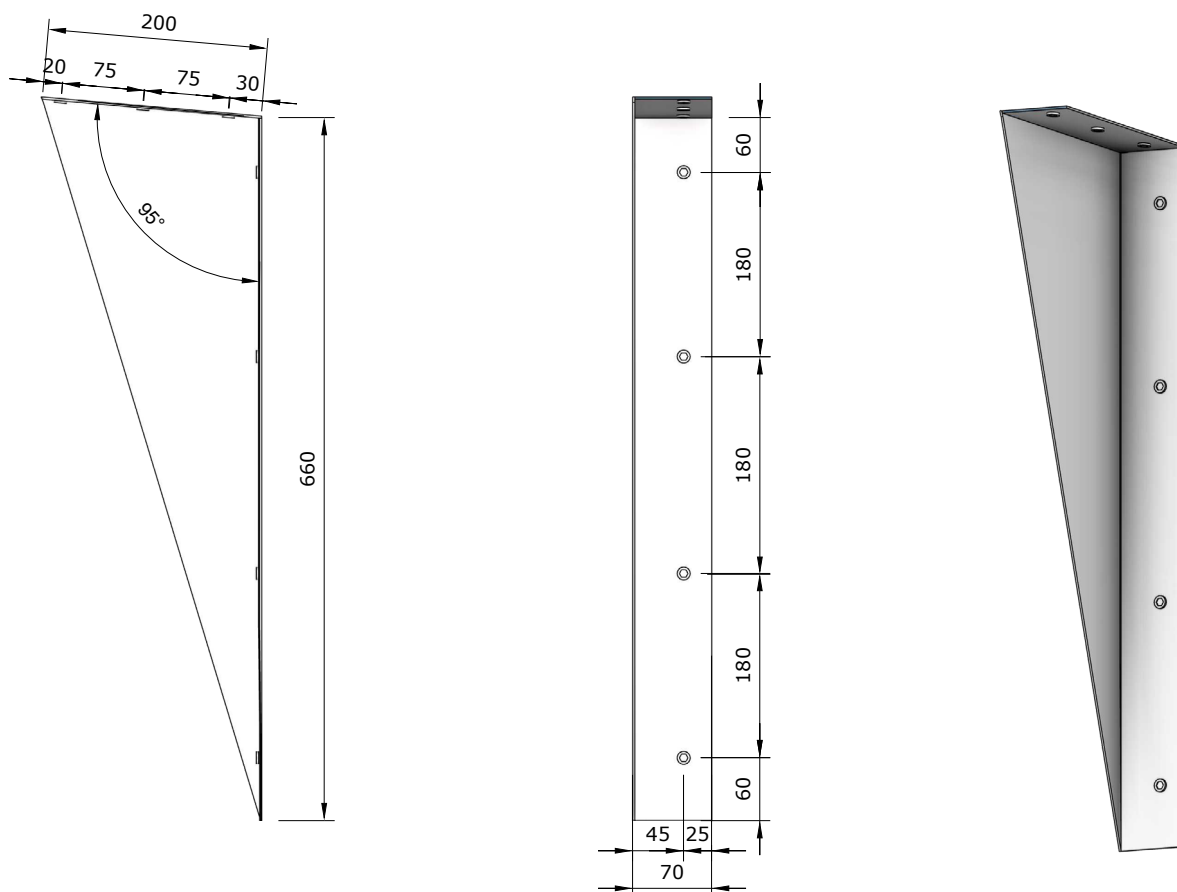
Ansichten des Stützbleches mit der Vermassung der Befestigung, Masse in mm.
